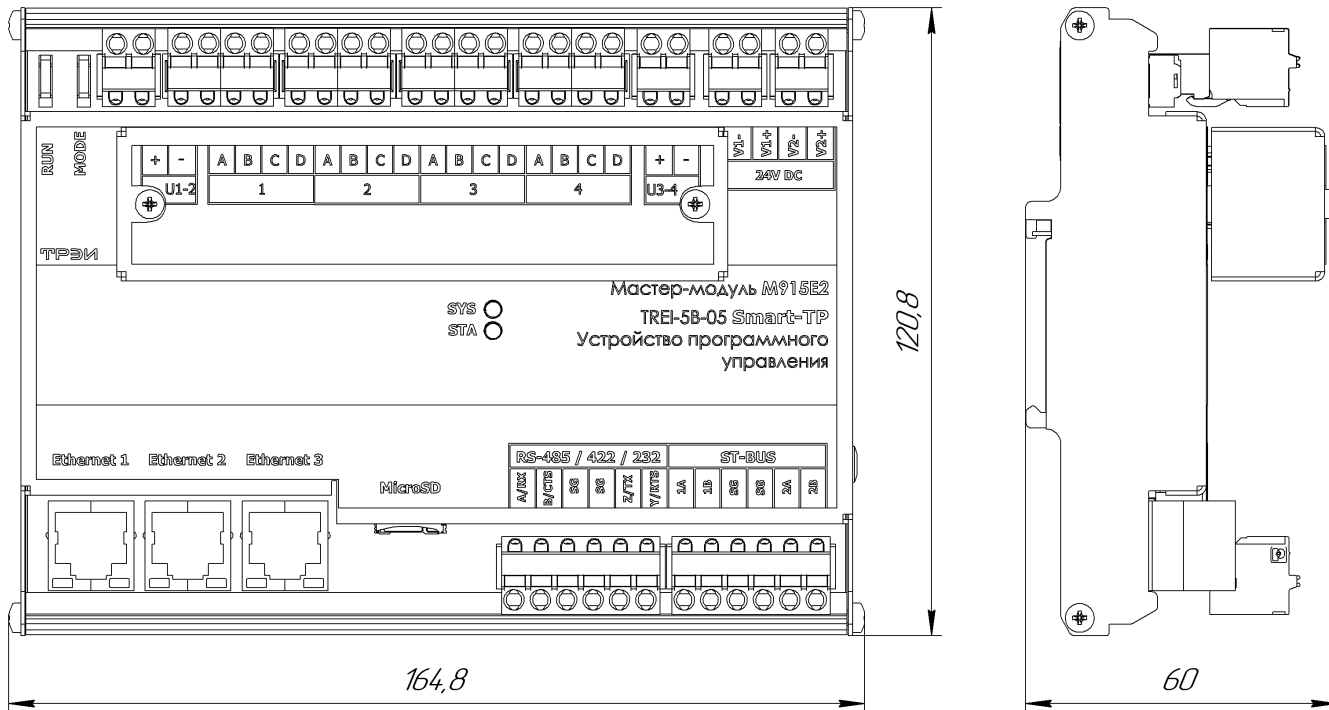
Чертеж общего вида M915E2 с указанием габаритных и присоединительных размеров
